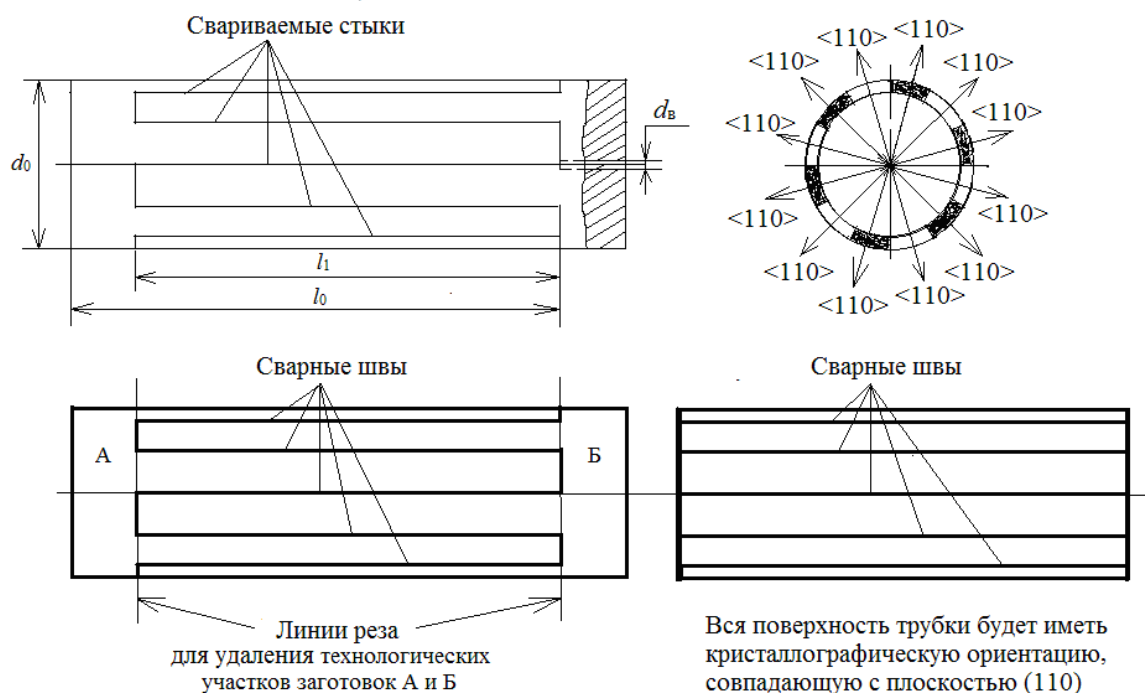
Электронно-лучевая сварка стыков и окончательная вырезка монокристаллического катода
